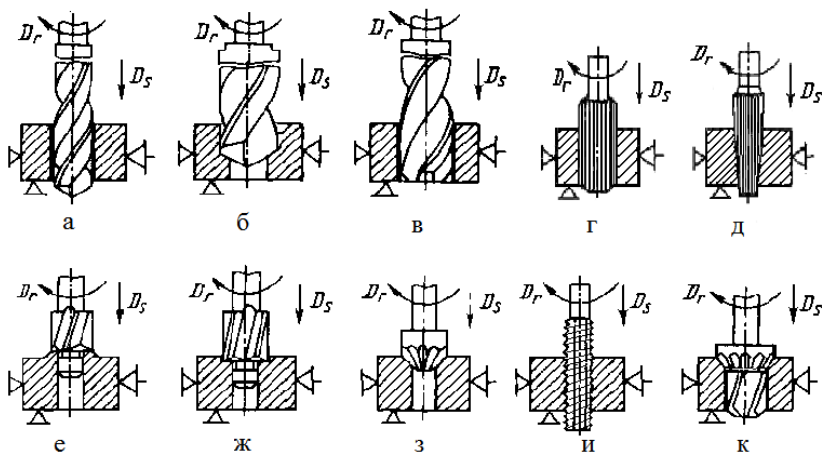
Схемы обработки заготовок осевым многолезвийным инструментом: а – сверление; б – рассверливание; в – зенкование; г, д – развертывание соответственно цилиндрического и конического отверстия; е, ж – цекование; з – зенкование; и – нарезание резьбы; к – обработка отверстия сложного профиля комбинированным инструментом (комбинированный зенкер)
